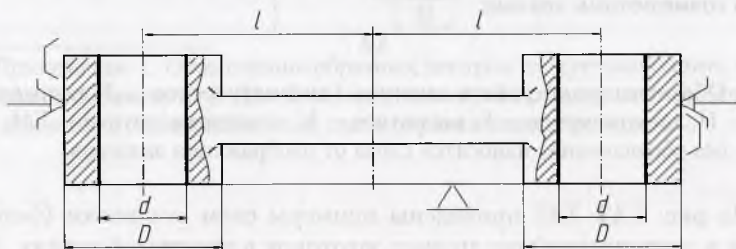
Схема установки заготовки в самоцентрирующих тисках с призматическими губками
